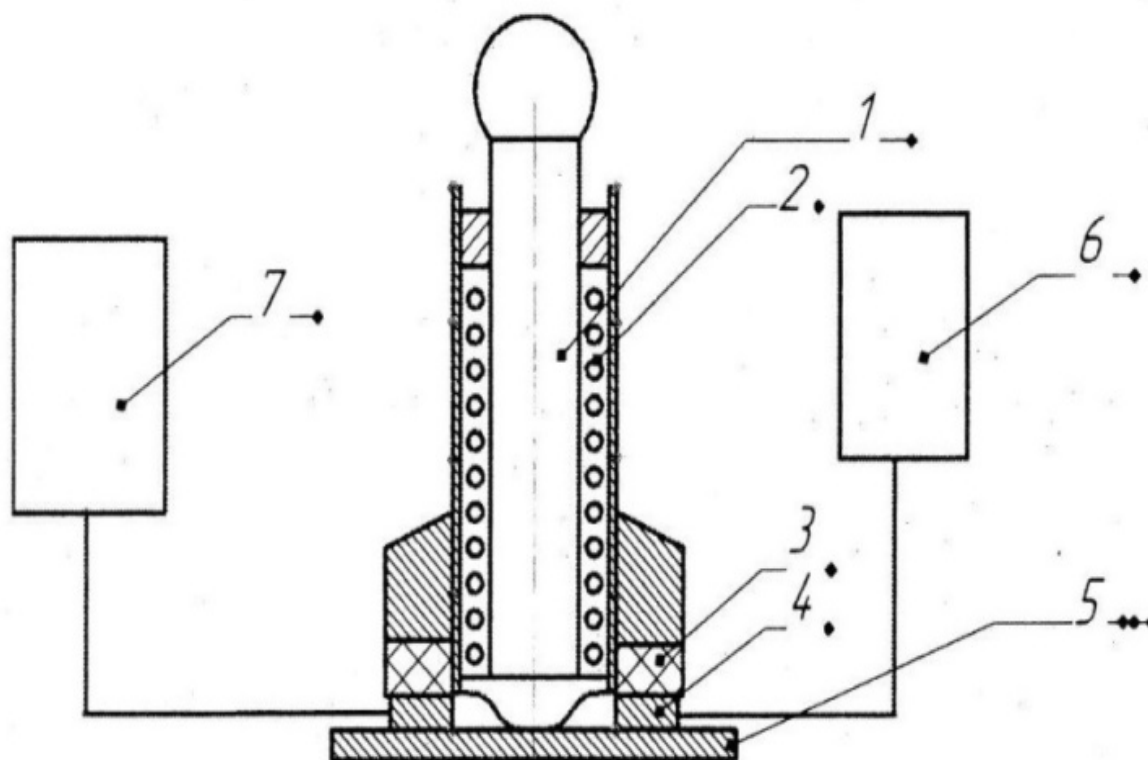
Устройство для ударного размагничивания.: 1-боек; 2-пружина; 3- намагничивающая катушка; 4-датчики магнитного поля; 5-деталь; 6-магнитометр; 7-генератор тока
